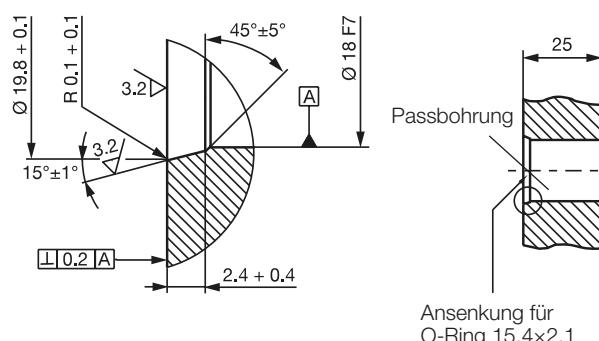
Passbohrung für die Montage des BTL mit O-Ring
